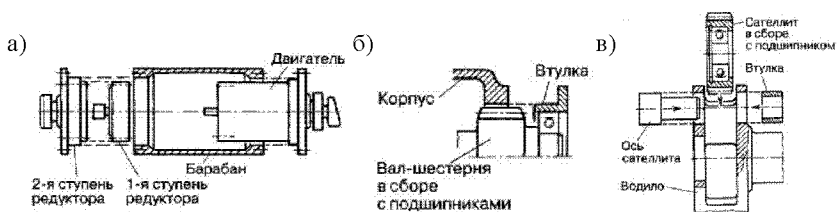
Конструктивные приемы обеспечения сборки
